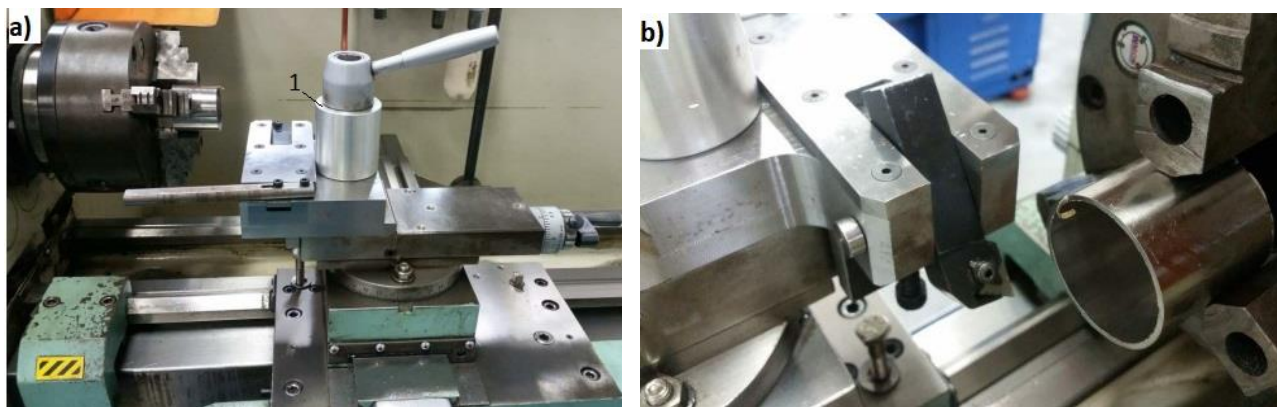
Dispositivo QSD montado no torno e acionado, com cavaco fixo à peça.
